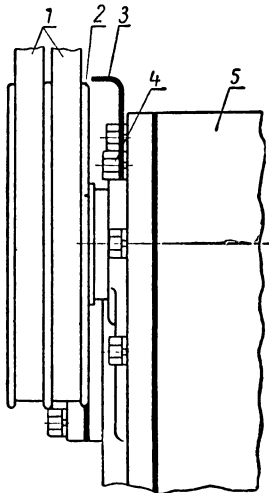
Установка стрелки для проверки угла опережения впрыска топлива:
